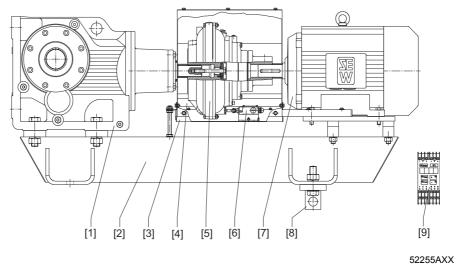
Keglerradgetiriebe auf Motorschwinge MK
